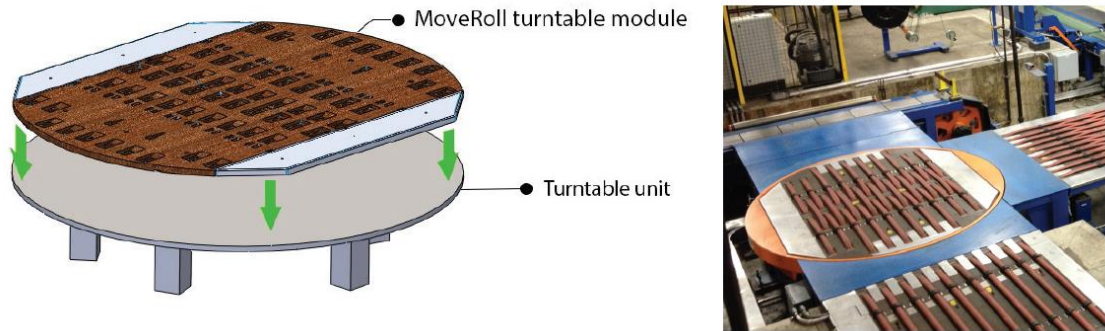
Moveroll kaltevan tason kuljetin [2.]
